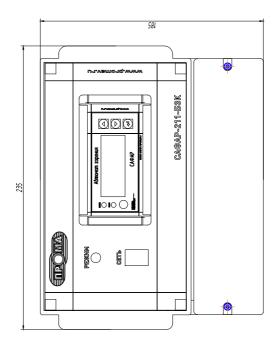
Конструкция и габаритные размеры автомата горения настенного исполнения Н.
